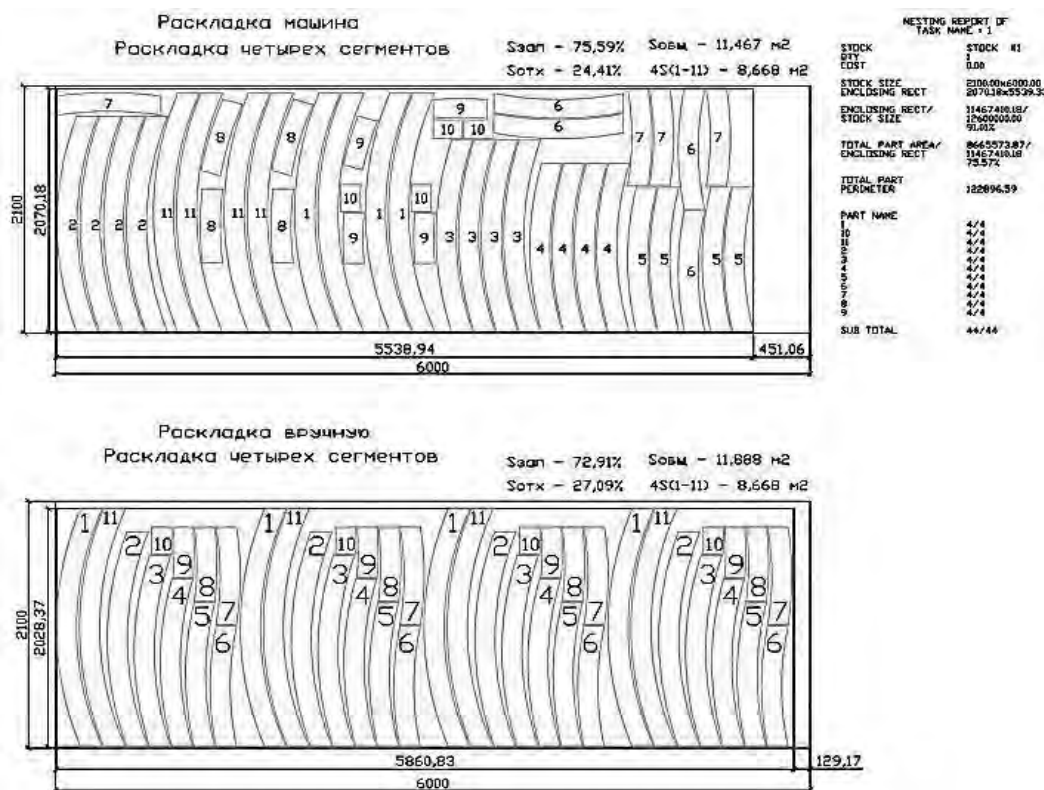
Раскрой прямоугольного листа пенополистирола на четыре вкладыша
